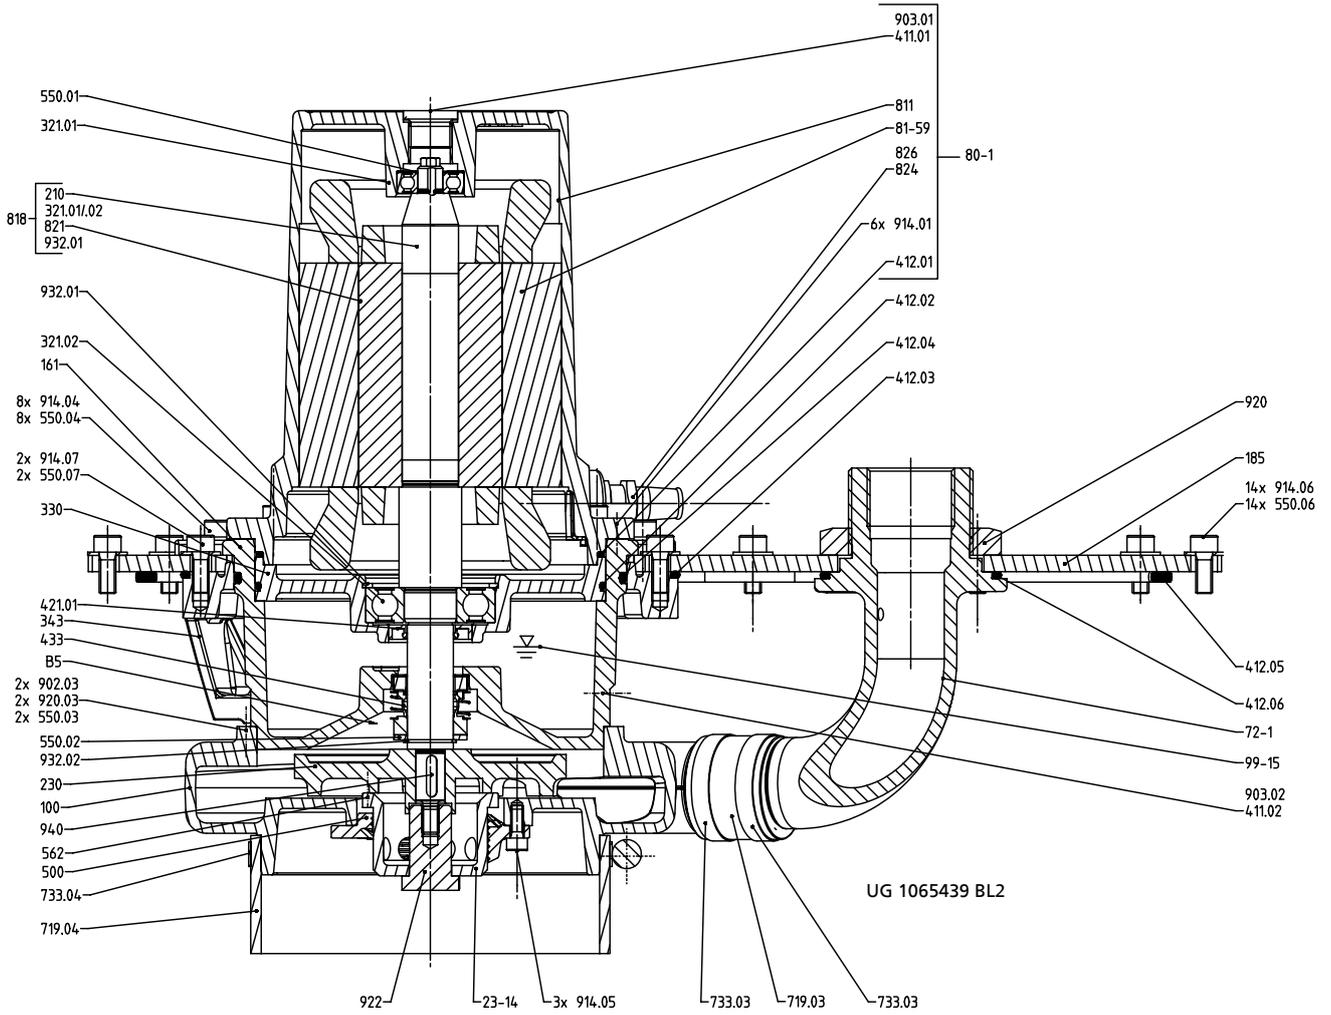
Обзорный чертеж US100, UZS150 - ходовая часть
